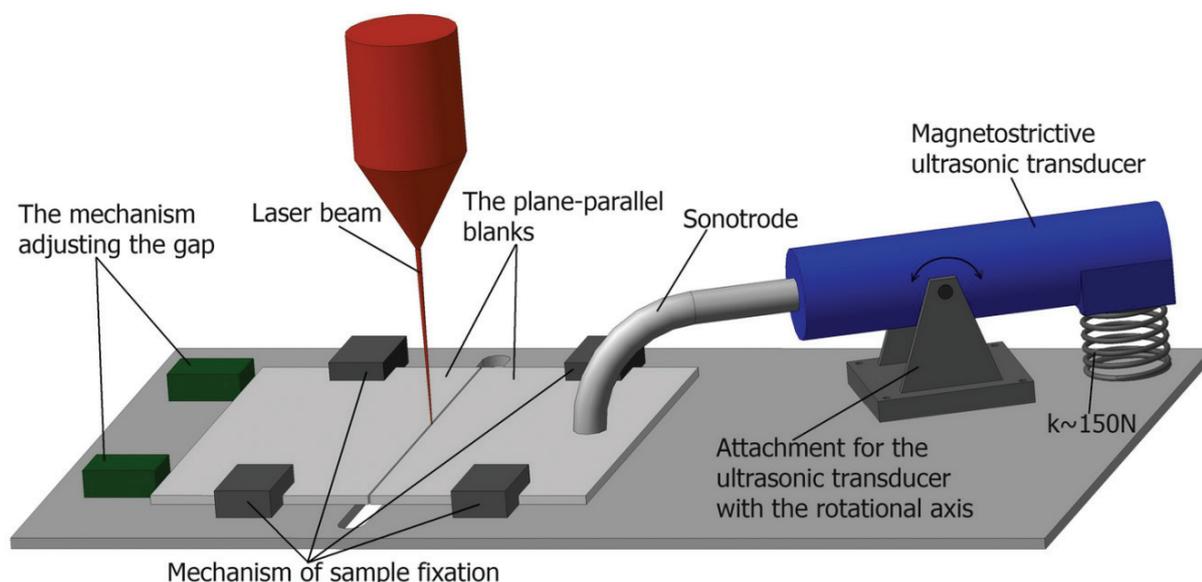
Схема установки лазерной сварки с ультразвуковым воздействием
